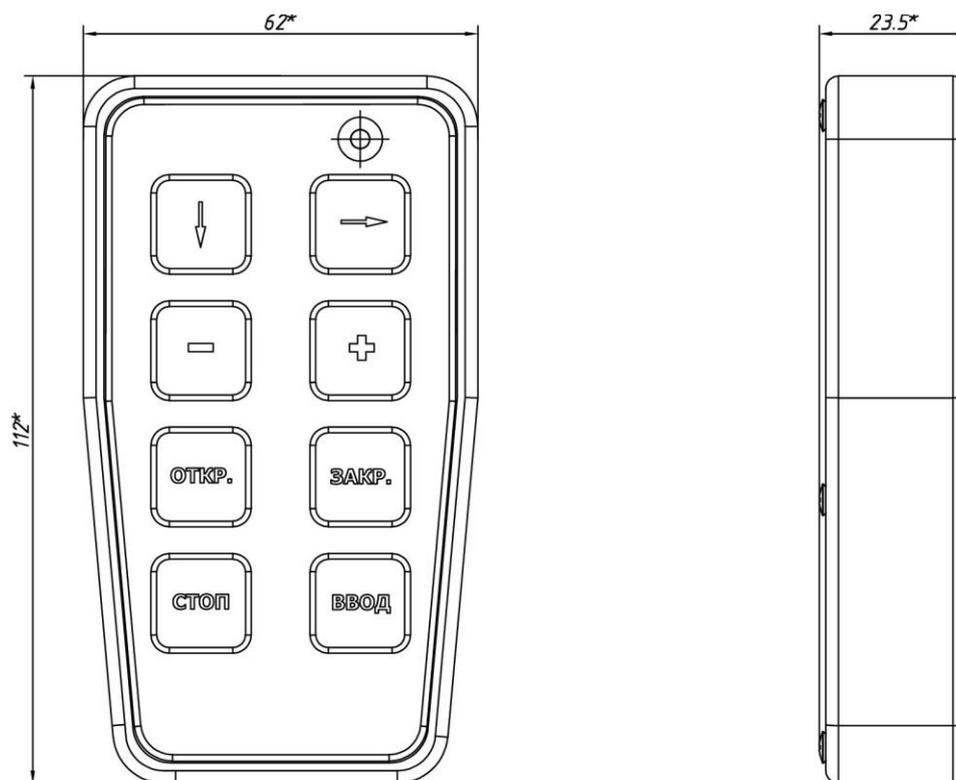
Внешний вид и габаритные размеры ПДУ-ВМ
